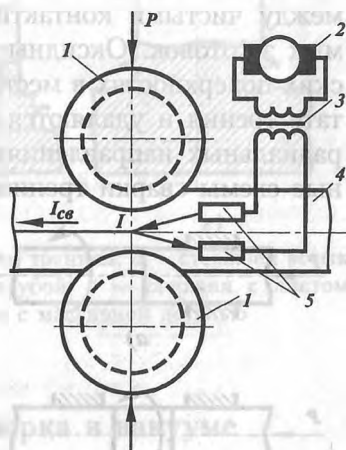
Принципиальная схема радиочастотной сварки: 1 — сжимающие ролики; 2 — ламповый генератор; 3 — трансформатор; 4 — движущаяся заготовка трубы; 5 — контакты;  $I_{св}$  — сварочный ток
